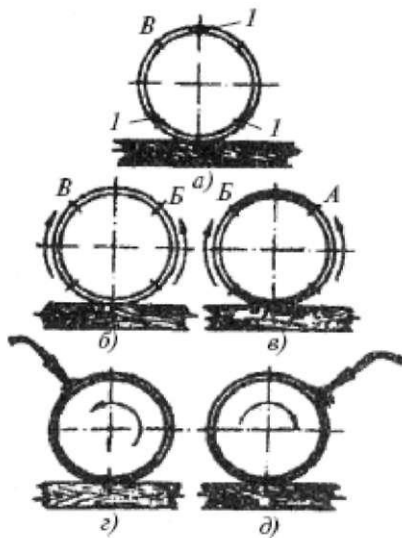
Порядок сварки стыков труб с поворотом: а - места размещения прихваток (1) и участков шва (А, Б, В, Г); б - выполнение первого слоя на участках А—Б и Г—В; в - поворот стыка и выполнение первого слоя на участках Г—А и В—Б; г - выполнение второго слоя шва, д - выполнение третьего слоя шва
